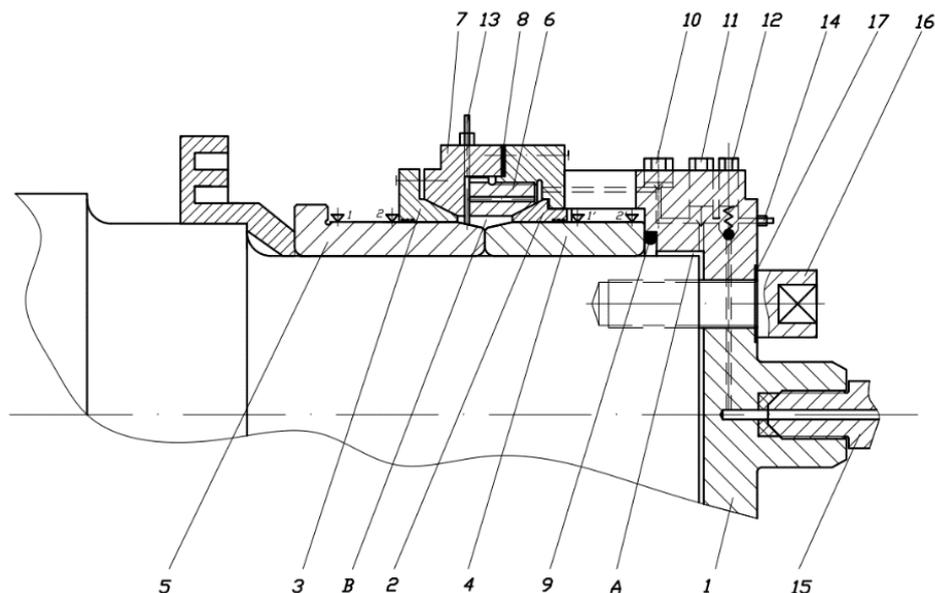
Принципиальная схема устройства для контроля напрессовки колец буксовых подшипников:
